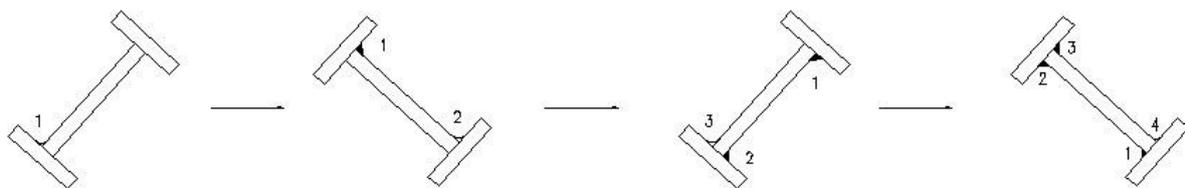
工字梁成柱组合焊缝（角焊缝）船形焊的焊接顺序
